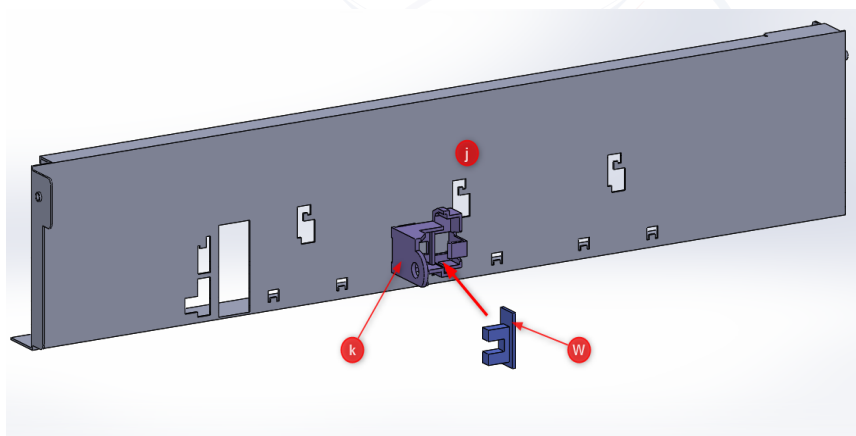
Montaje del sensor herradura (W) en el soporte (k)
